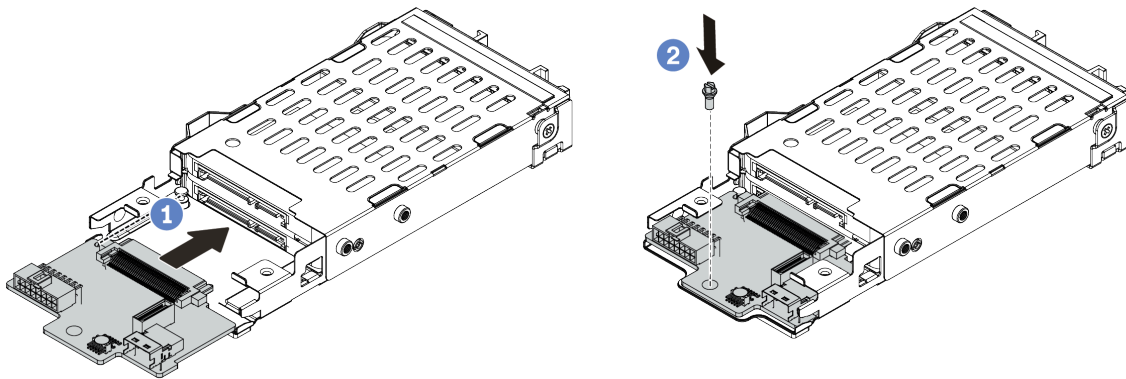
Installazione del backplane dell'unità da 7 mm (parte inferiore)
